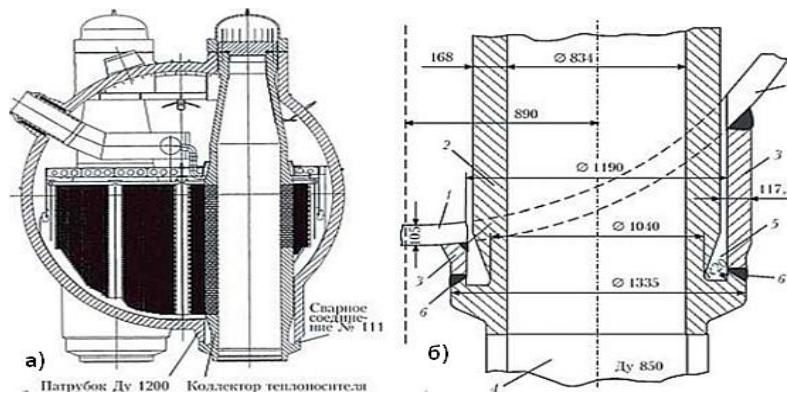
Узел соединения коллектора с парогенератором: а – сечение ПГВ1000МКП; б – схема расположения сварного соединения №111: 1 – корпус ПГВ; 2 – коллектор; 3 – патрубок Ø 1200 мм; 4 – трубопровод ГЦТ Ø 850 мм; 5 – карман; 6 – шов №111
